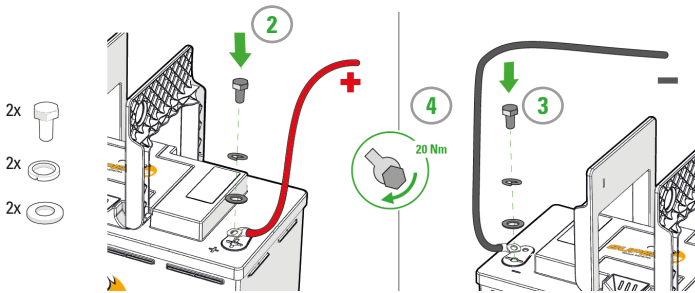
Plaats de handgrepen over de aansluitklemmen
